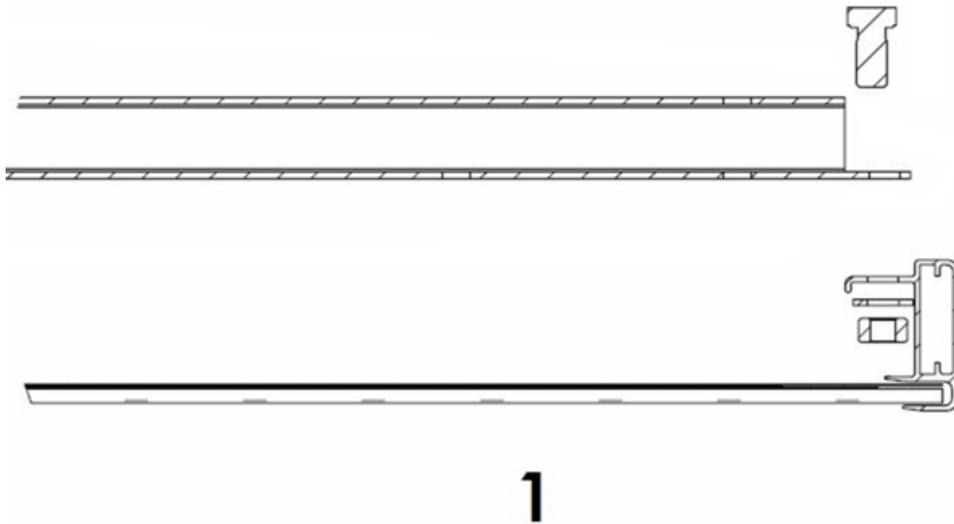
Detailansicht Backrail bzw. Modul (Schnitt) zur Montage der Backrails (Ansicht von unten)
